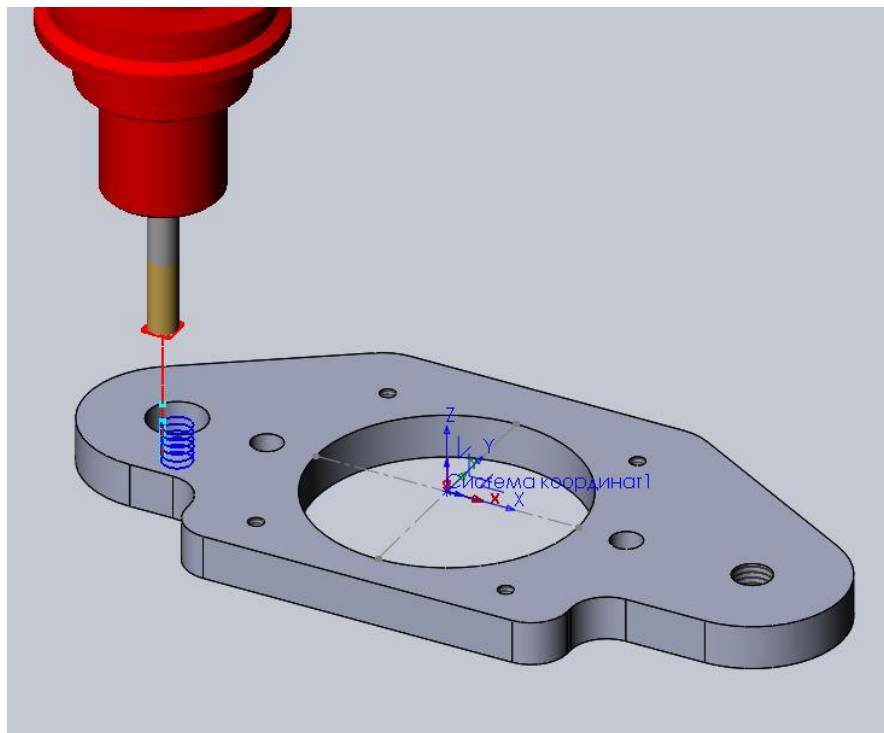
Фрезерування внутрішнього контуру отвору Ø16 мм
